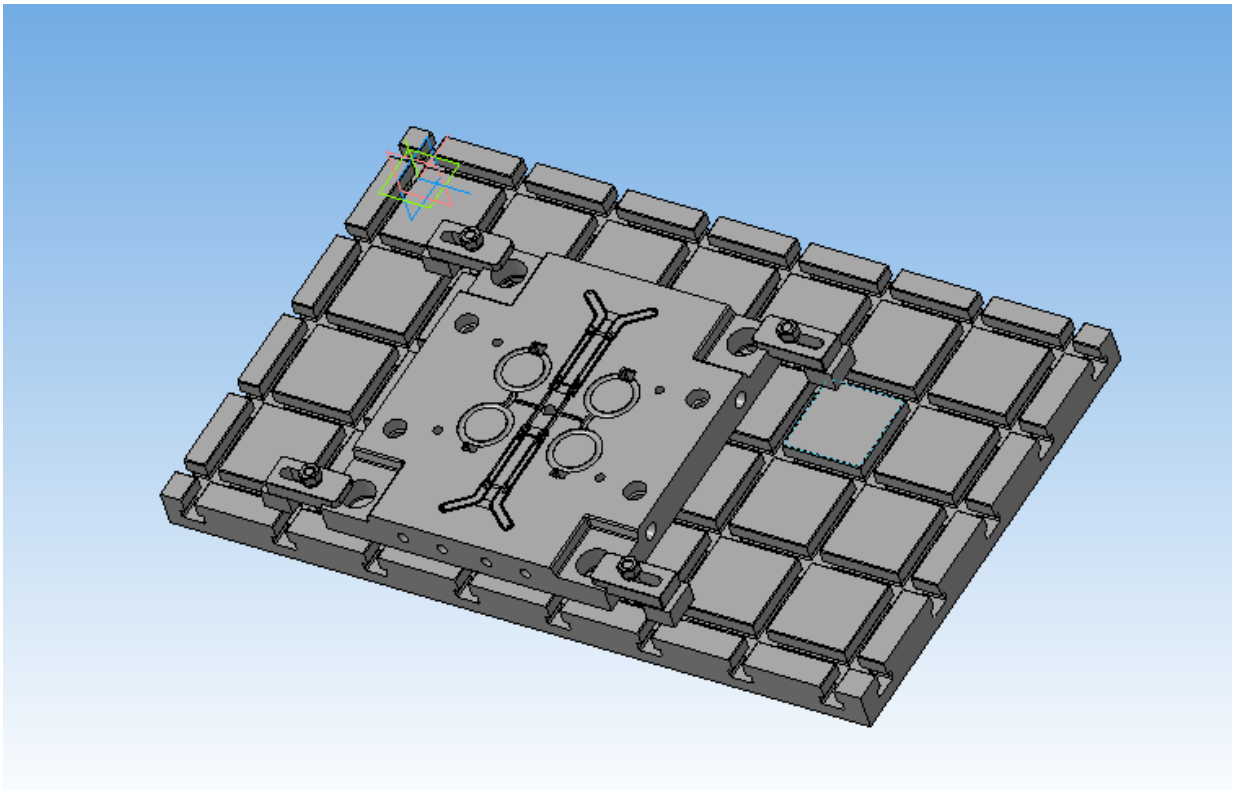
Операційний ескіз операції при фрезерування формуючих поверхонь
